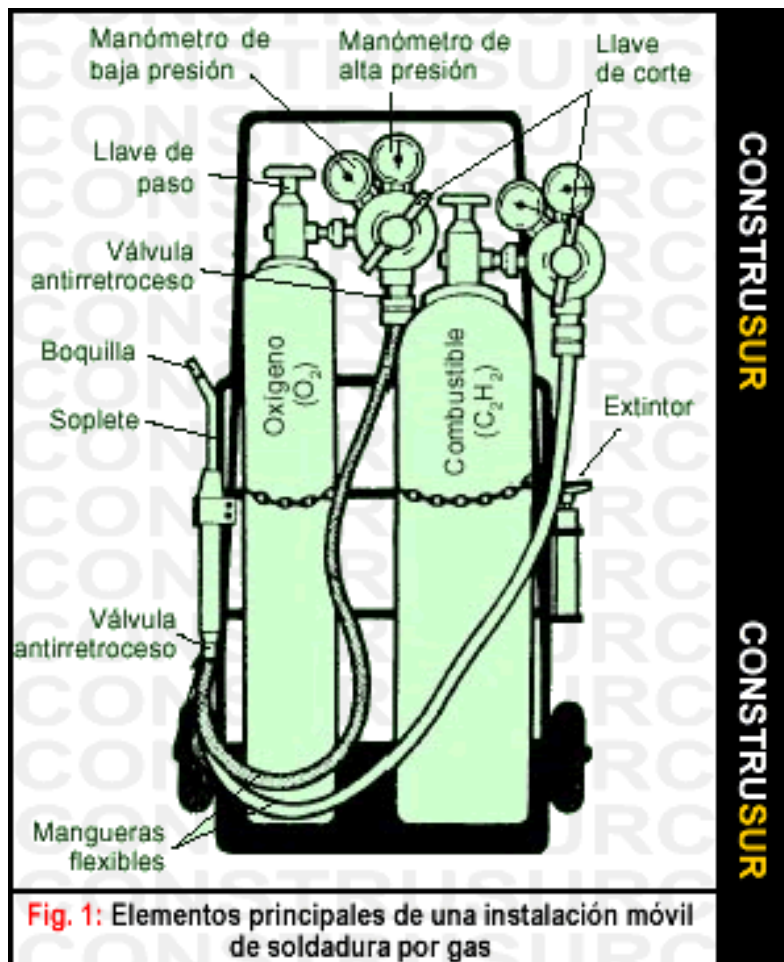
Equipo para soldadura con oxiacetileno
